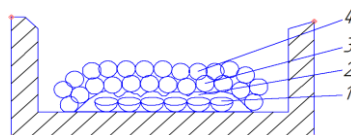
Оплавление и обволакивание шлакоактивными элементами модификатора: 1 - модификатор; 2 - шлак магнитоактивный; 3 - лигатура; 4 - чугун дробленый со шлакообразующими добавками
